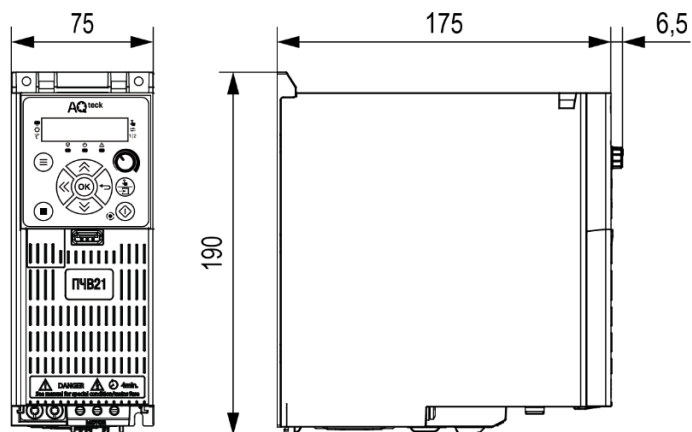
Габаритні розміри ПЧВ у корпусі 4
